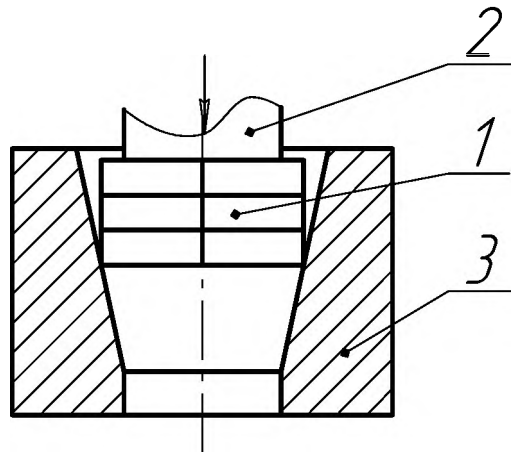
Переформування заготовок продавлюванням через матрицю
